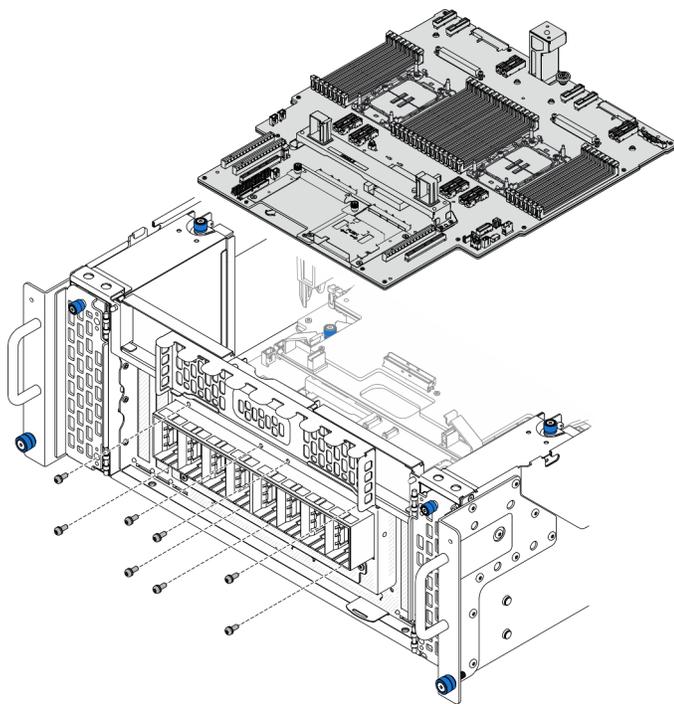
Entfernen der Schrauben des UPI-Moduls
